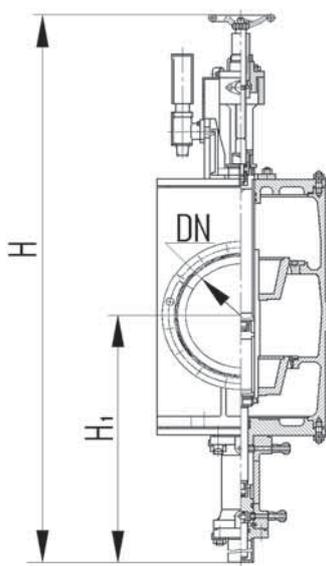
Клапан регулирующий проходной фланцевый с гидроприводом
